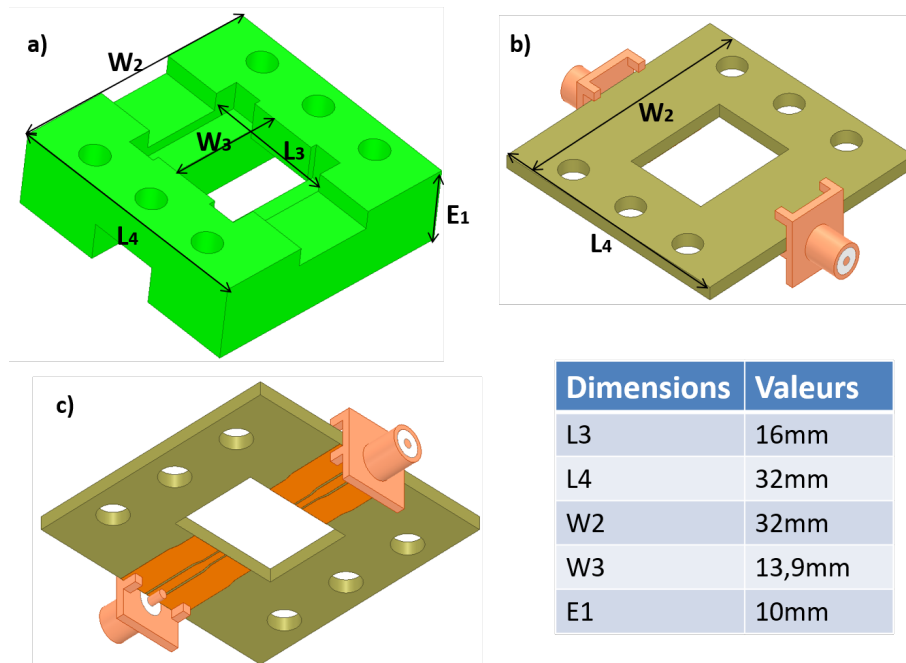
a- Support 3D, b- Vue du dessus du PCB, b- Vue du dessous du PCB
